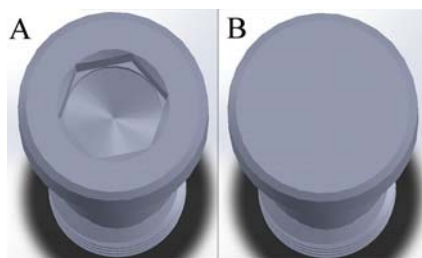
(A) Corte hexagonal parafuso protético CM, (B) Remoção do encaixe.
